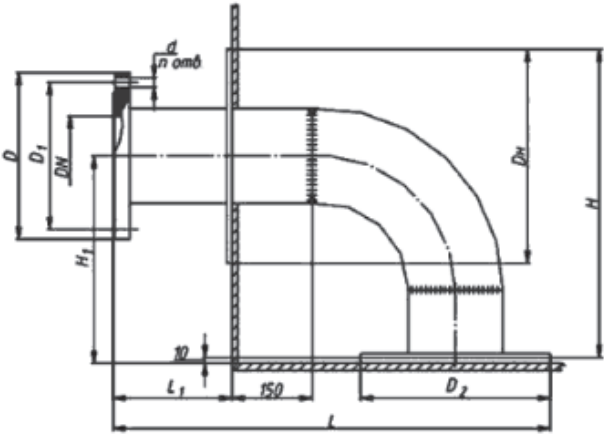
Общий вид патрубка зачистного ПЗ
